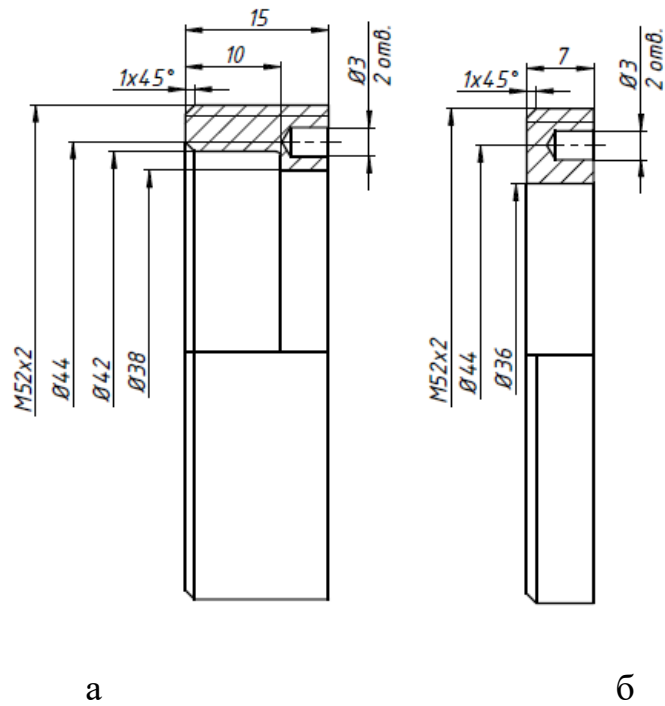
а – підшипникова втулка із зовнішньою різзю; б – стопорна втулка
